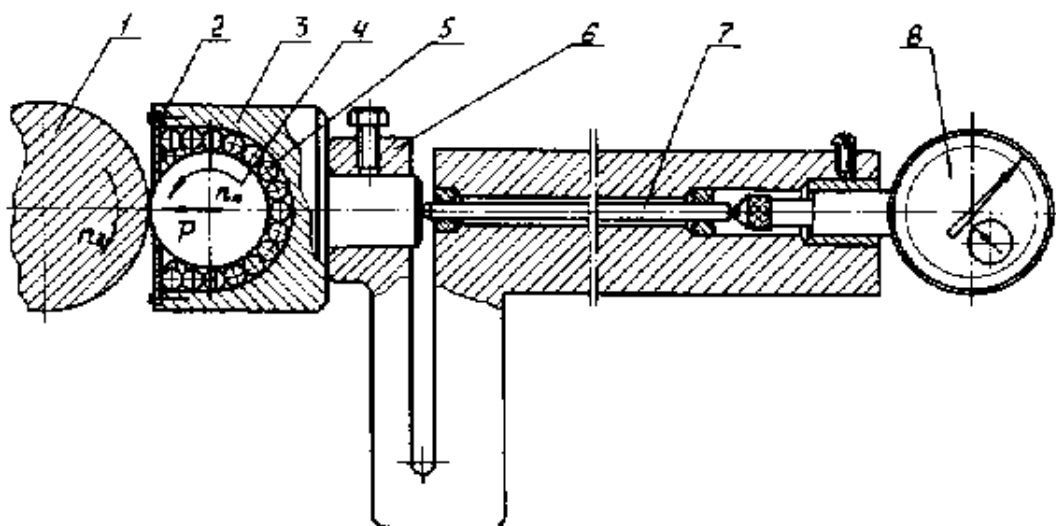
Інструмент для обробки обкаткою з вимірювальними приладами.
